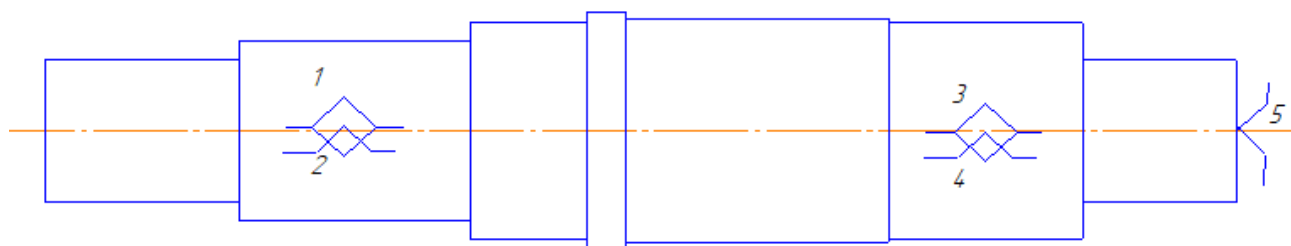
Закріплення заготовки на шпоночно-фрезерних операціях
